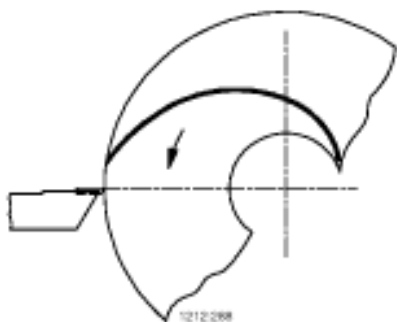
Направление вращения при обтачивании сварного колеса из хромникелевой стали
